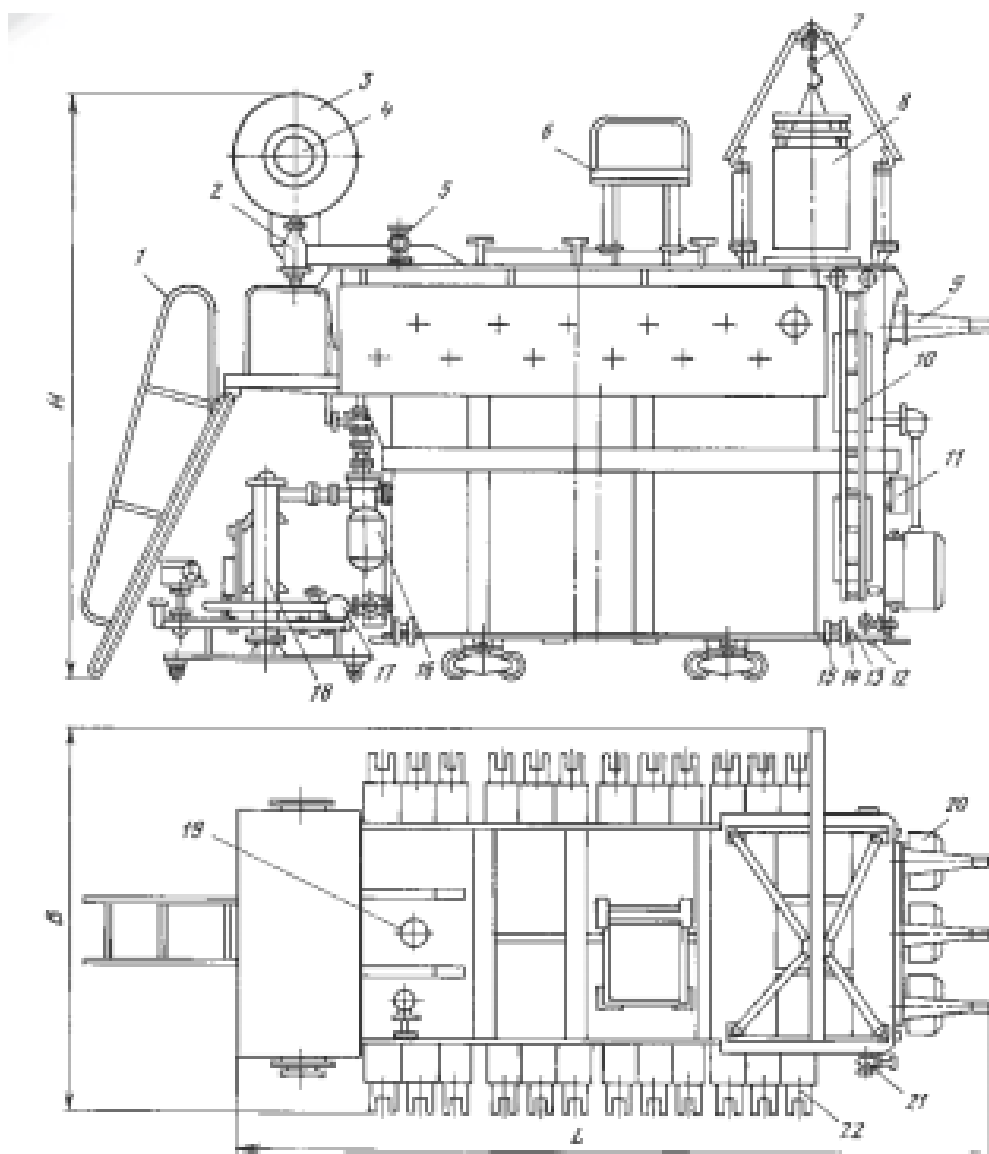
Общий вид и габаритные размеры трансформаторов ТЦНП
